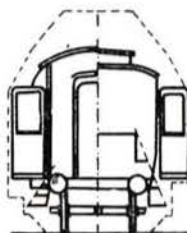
Gegenüberstellung von Tonnendach und Dach mit Oberlichtaufbau
